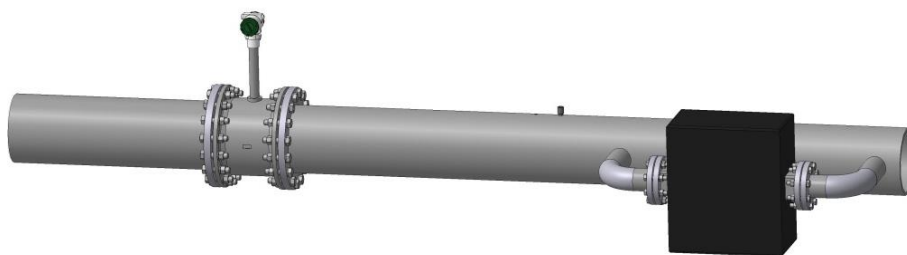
Монтаж ТЭГ на трубопровод
